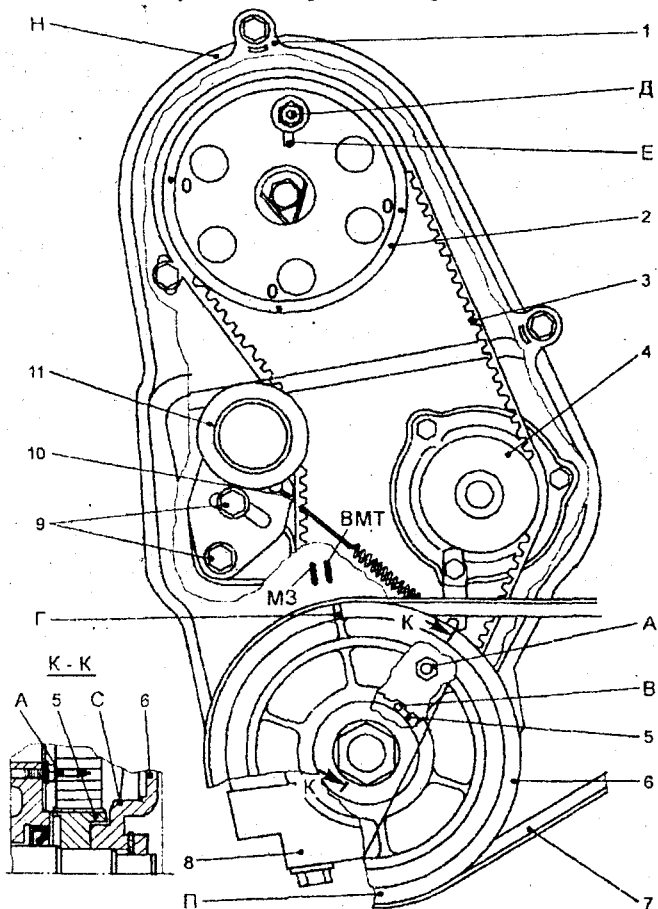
Привод распределительного вала и водяного насоса: 1 - наружный кожух; 2 - ведомый шкив распределительного вала; 3 - зубчатый ремень; 4 - шкив водяного насоса; 5 - ведущий шкив; 6 - шкив привода генератора; 7 - ремень привода генератора; 8 - упор наружного кожуха; 9 - болты; 10 - пружина; 11 - натяжной ролик.
